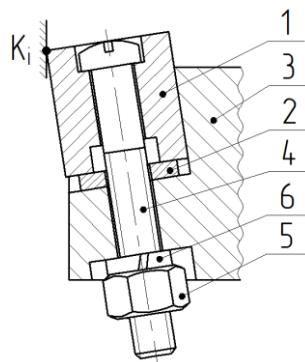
Способ настройки главной базовой точки K_i режущей пластины: 1 – СМП; 2 – опорная пластина; 3 – нож; 4 – винт; 5 – гайка; 6 – пружинная шайба.
